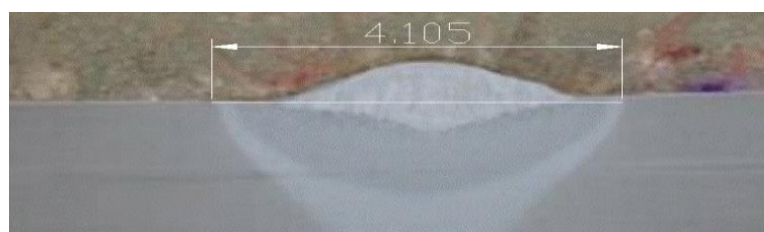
Medidas da LZAC utilizando software Inspetor de Solda®.
